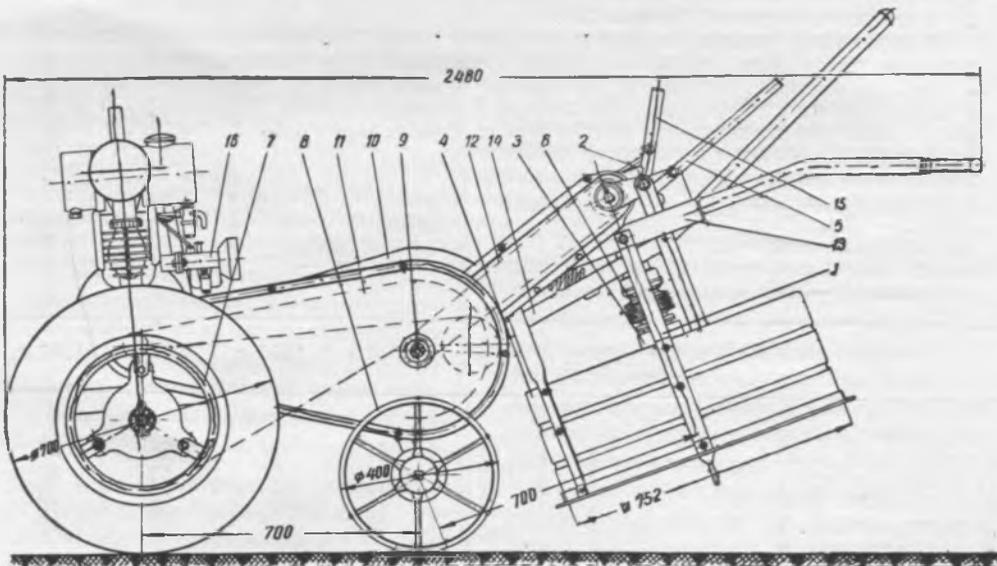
Самоходная центробежная мотыга: 1 — редуктор к почвенной фрезе в сборе; 2 — редуктор; 3 — почвенная фреза; 4 — кожух фрезы; 5 — рычаг для включения редуктора; 6 — защитный кожух; 7 — ведущие колеса; 8 — опорные колеса; 9 — промежуточный вал; 10 — передача к ведущим колесам; 11 — передача от двигателя; 12 — передача к редуктору; 13 — рама; 14 — механизм подачи; 15 — рычаг выключения муфт; 16 — двигатель с редуктором
